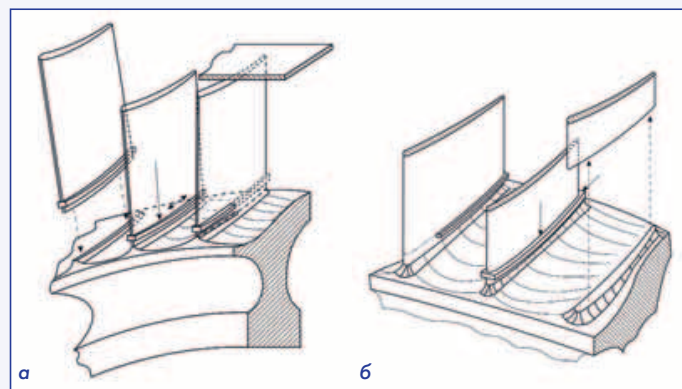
Изготовление моноколес с помощью сварки трением:
